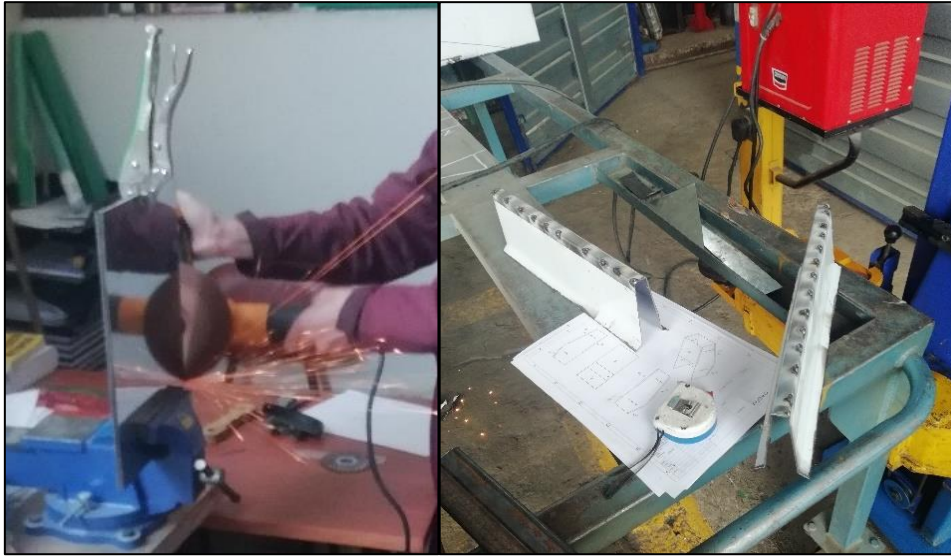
Corte de las planchas y construcción de las aletas del batidor.
